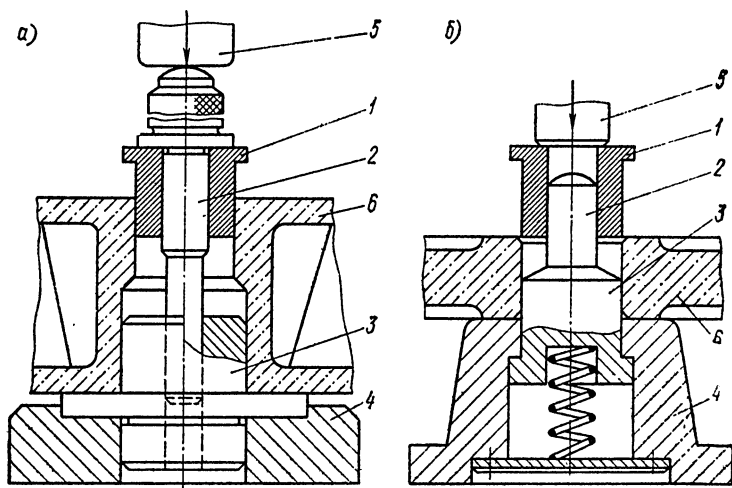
Схемы запрессовок подшипниковых втулок с использованием приспособлений
